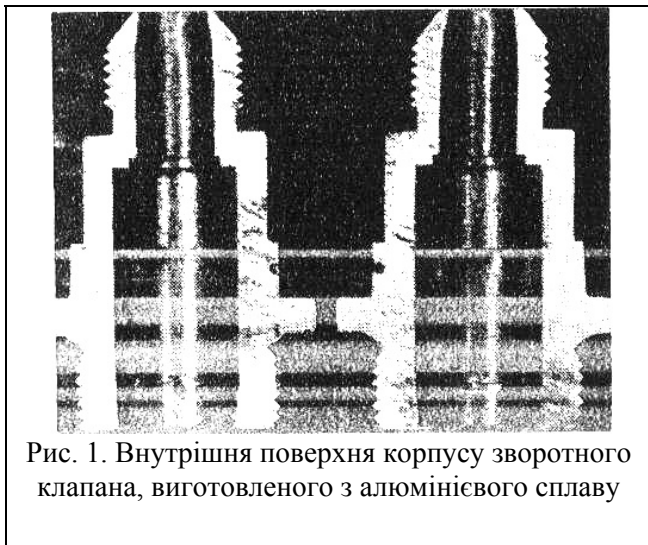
Внутрішня поверхня корпусу зворотного клапана, виготовленого з алюмінієвого сплаву
